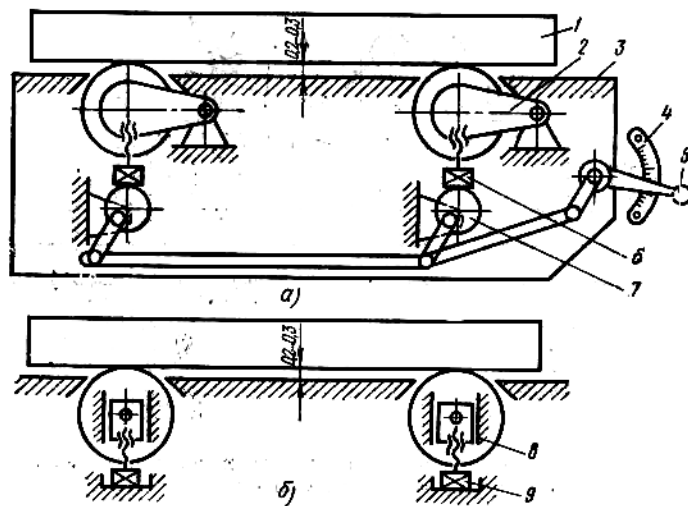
Схема регулировки опорных роликов в столе рейсмусового станка:
